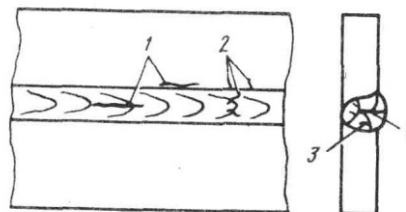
Расположение горячих трещин в сварном соединении:
